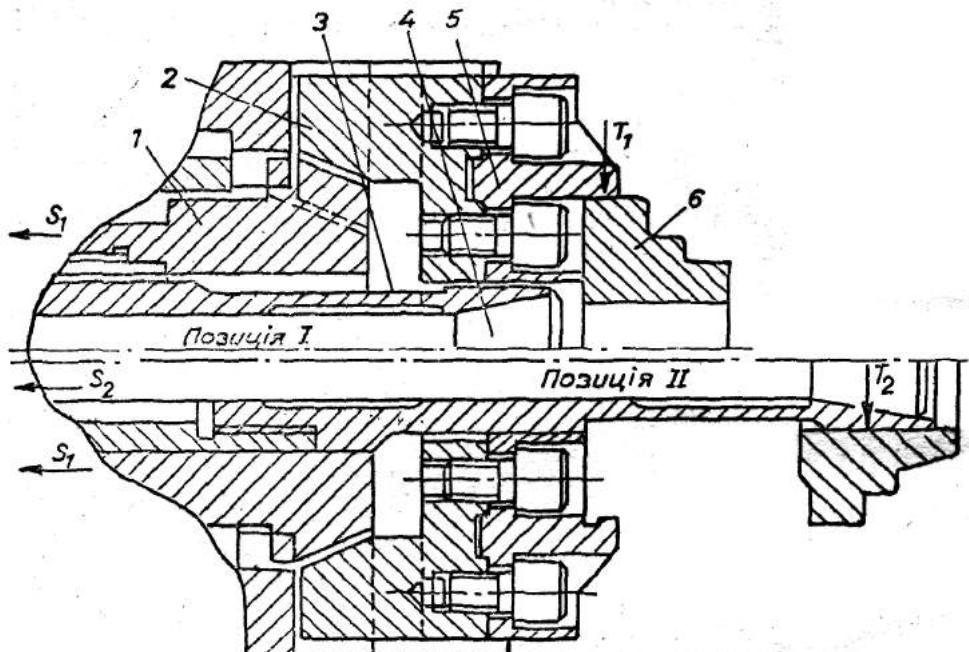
Введення додаткового вузла у затискний пристрій токарного верстата з ЧПК:
